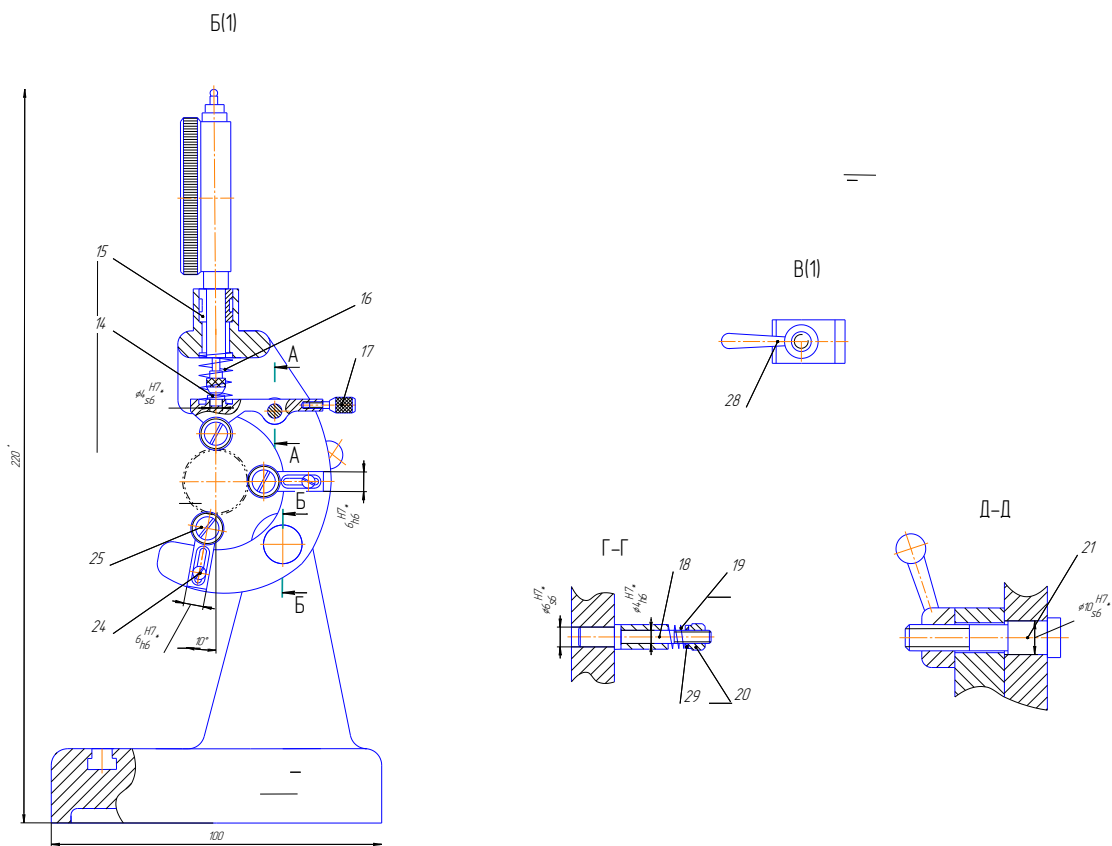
Приспособление для контроля метрической резьбы (вид справа)
